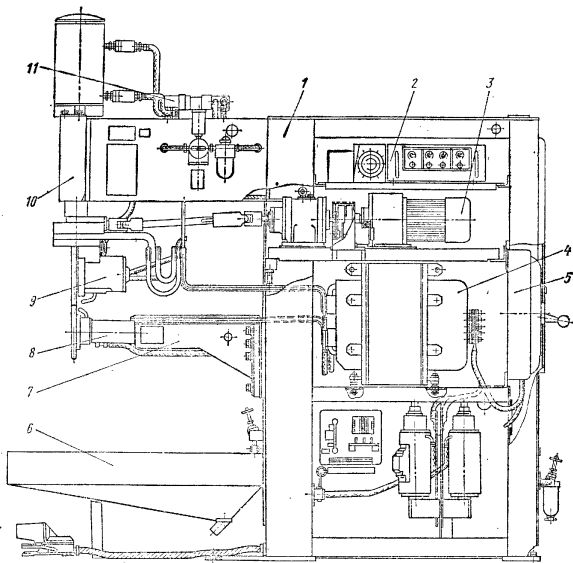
Машина типа МШ-3201 для шовной сварки
